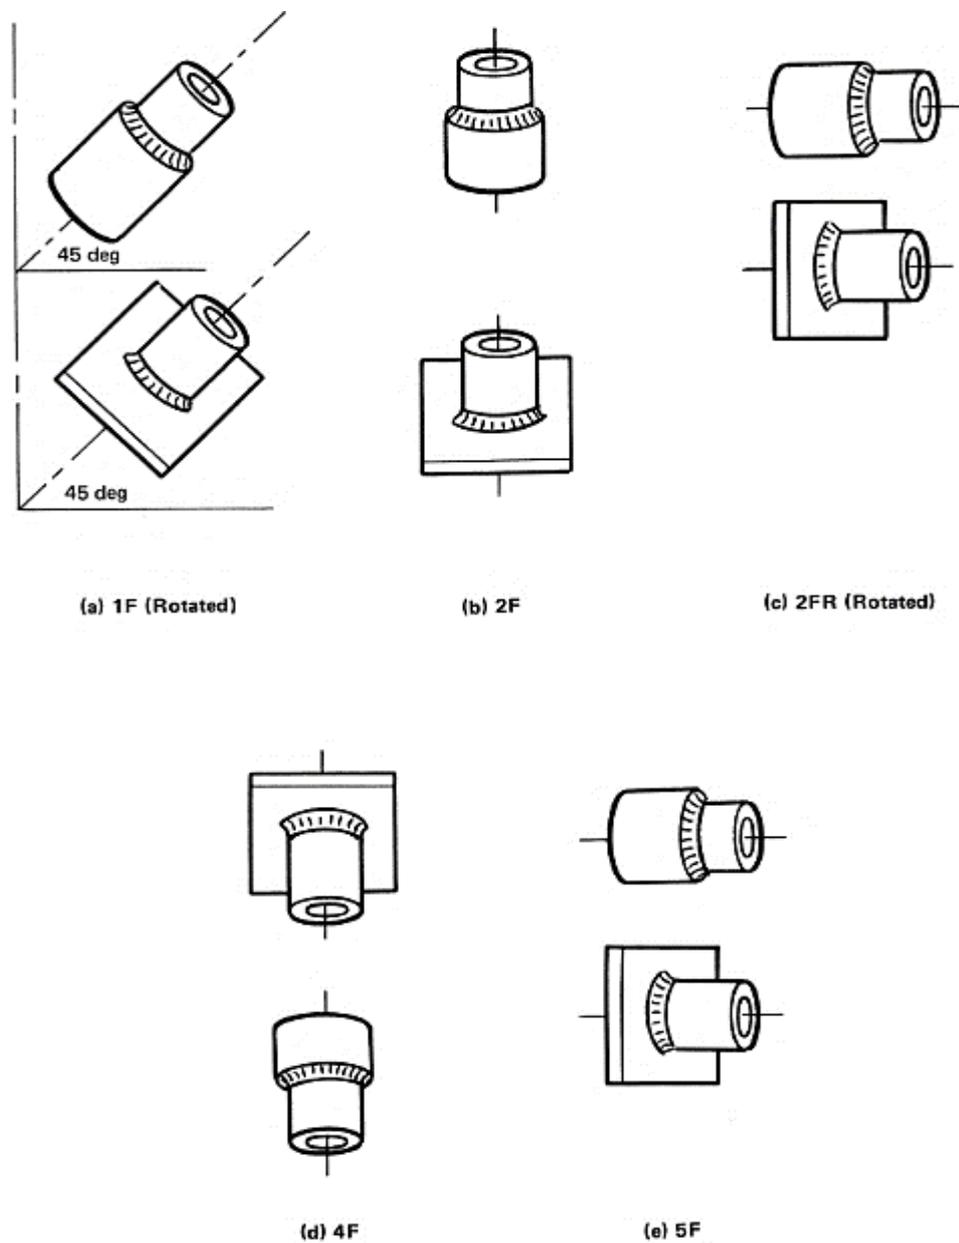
Posiciones de soldadura para tubería en filete.
